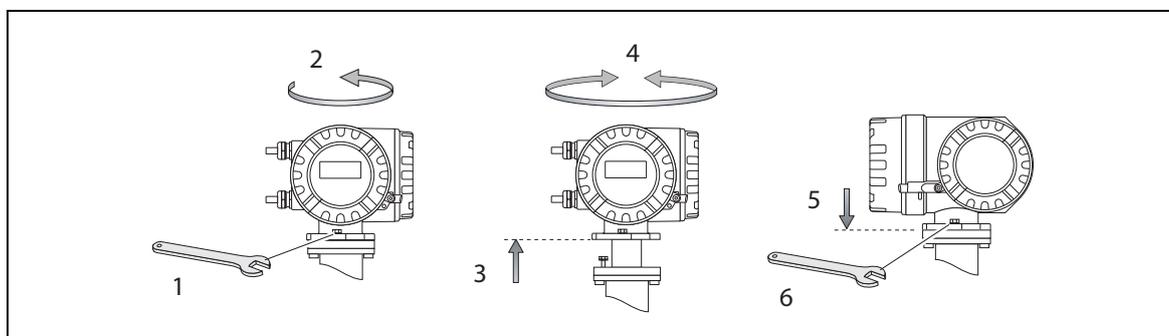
Поворот корпуса преобразователя (в алюминиевом рабочем корпусе)
